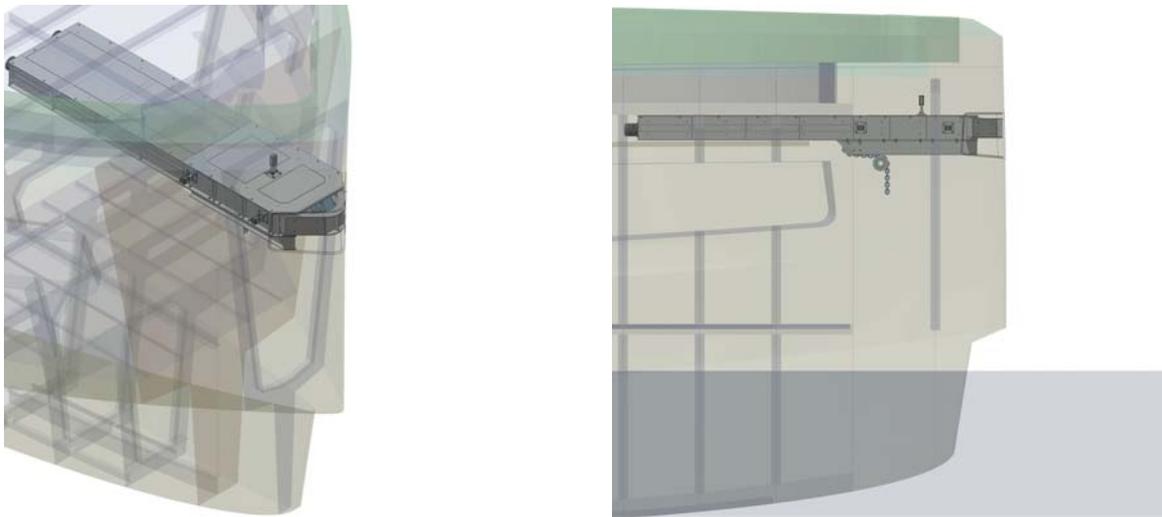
Im Bug eingebaute Ankerlade mit eingefahrener Lade, transparente Darstellung
